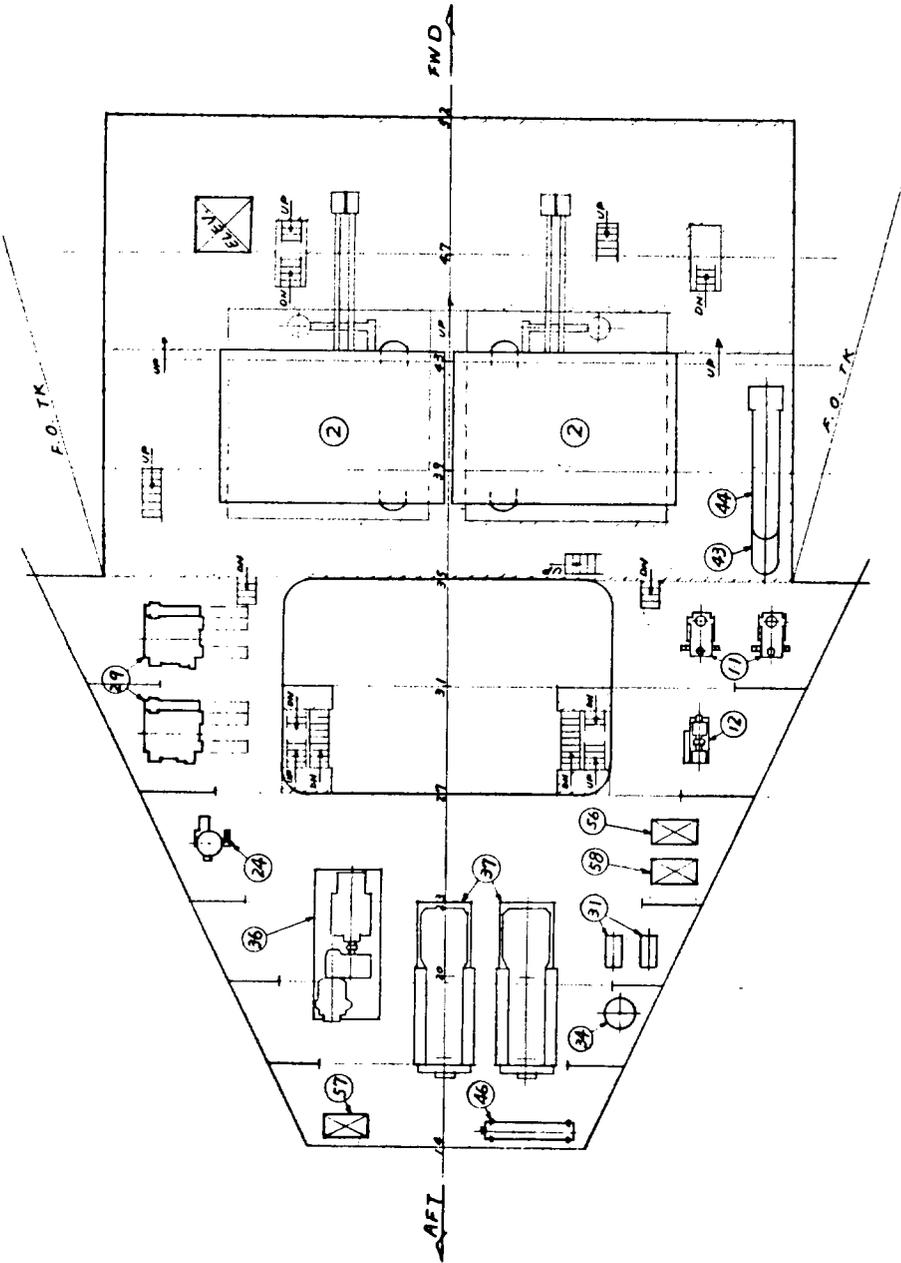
3. 1-12 (F-1) 船舶イラ笠型 C.O.P.T. LOWER FLOOR PLAN
